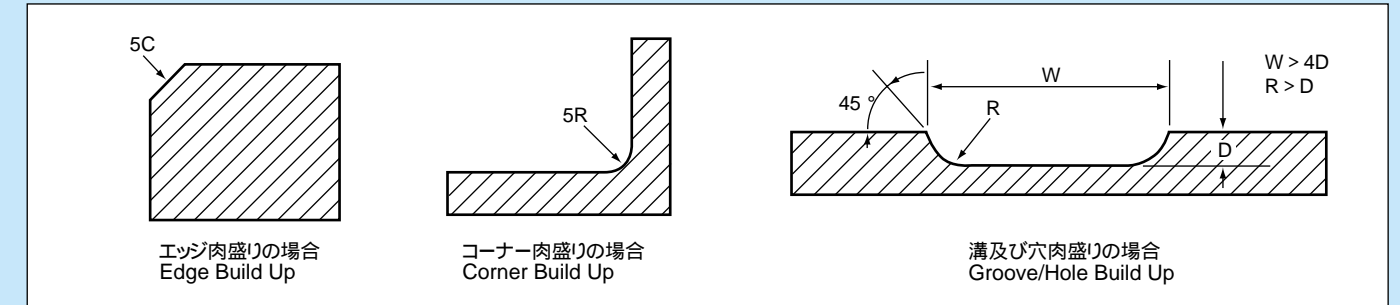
肉盛り溶接における標準開先形状 Figure 1. Standing shapes for build up welding
